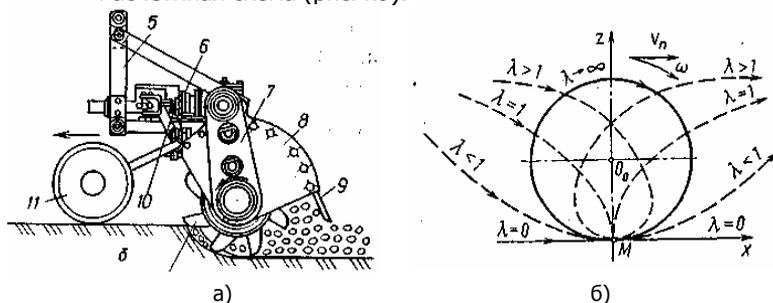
Расчетная схема: а - общий вид навесной фрезерной машины; 5 - навеска; 6 и 7 - редукторы; 8 - кожух; 9 - решетка; 10 - регулятор глубины; 11 - опорное колесо; б - схема траекторий движения точки ротора при различных кинематических параметрах λ .
